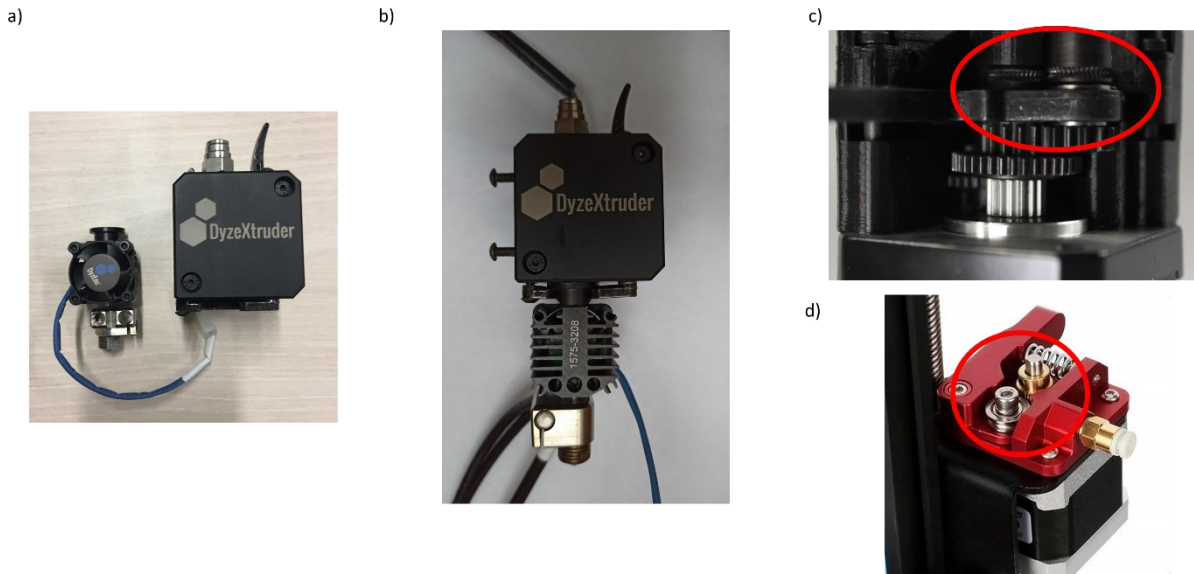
Le hot end et l'extruder de la marque DyzeDesign (a) À gauche le DyzeEnd-X Hotend, à droite le DyzeXtruder GT (b) Photo de l'assemblage du hot end et de l'extruder DyzeDesign (c) Extruder à double engrenages dentés (d) Extruder à simple engrenage denté
